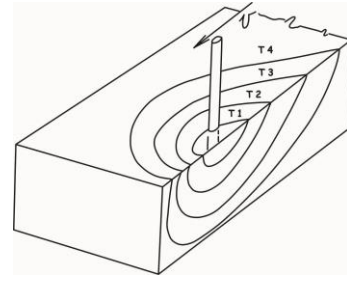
Isothermas na soldagem de placas grossas (três dimensões)
